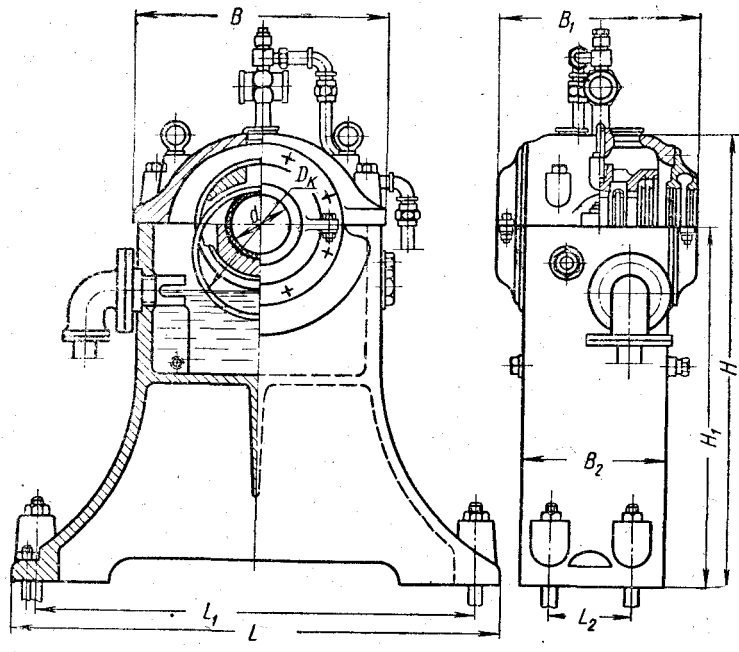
Подшипник стояковый с кольцевой смазкой.
